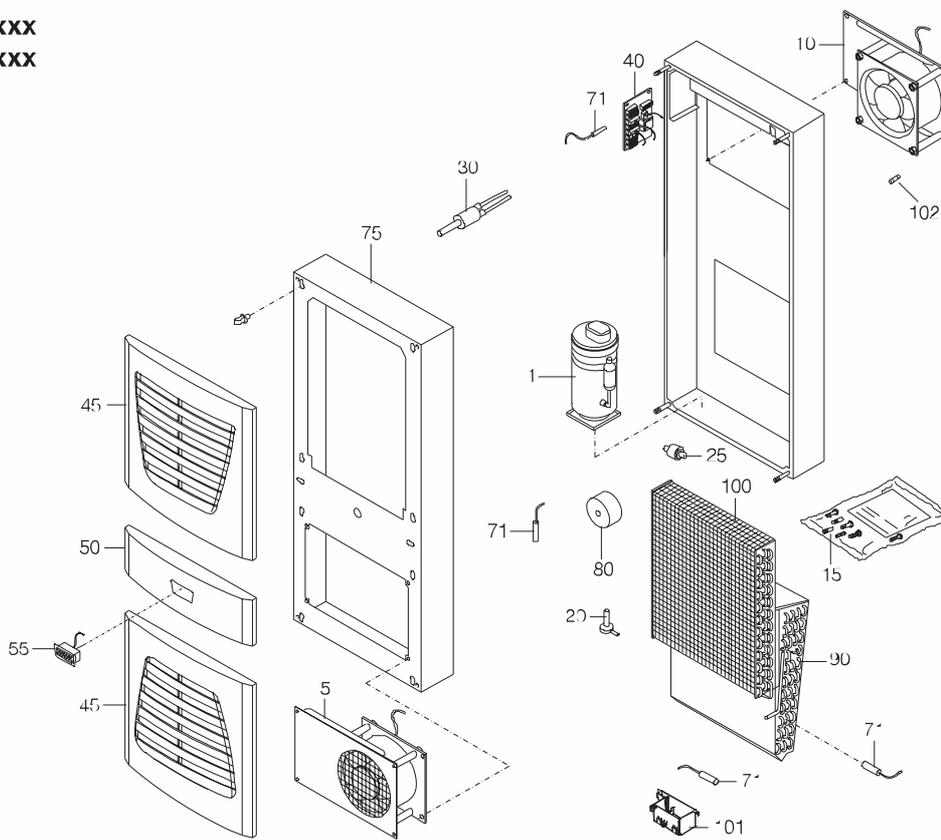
Parti di ricambio per SK 3304.xxx, SK 3305.xxx
